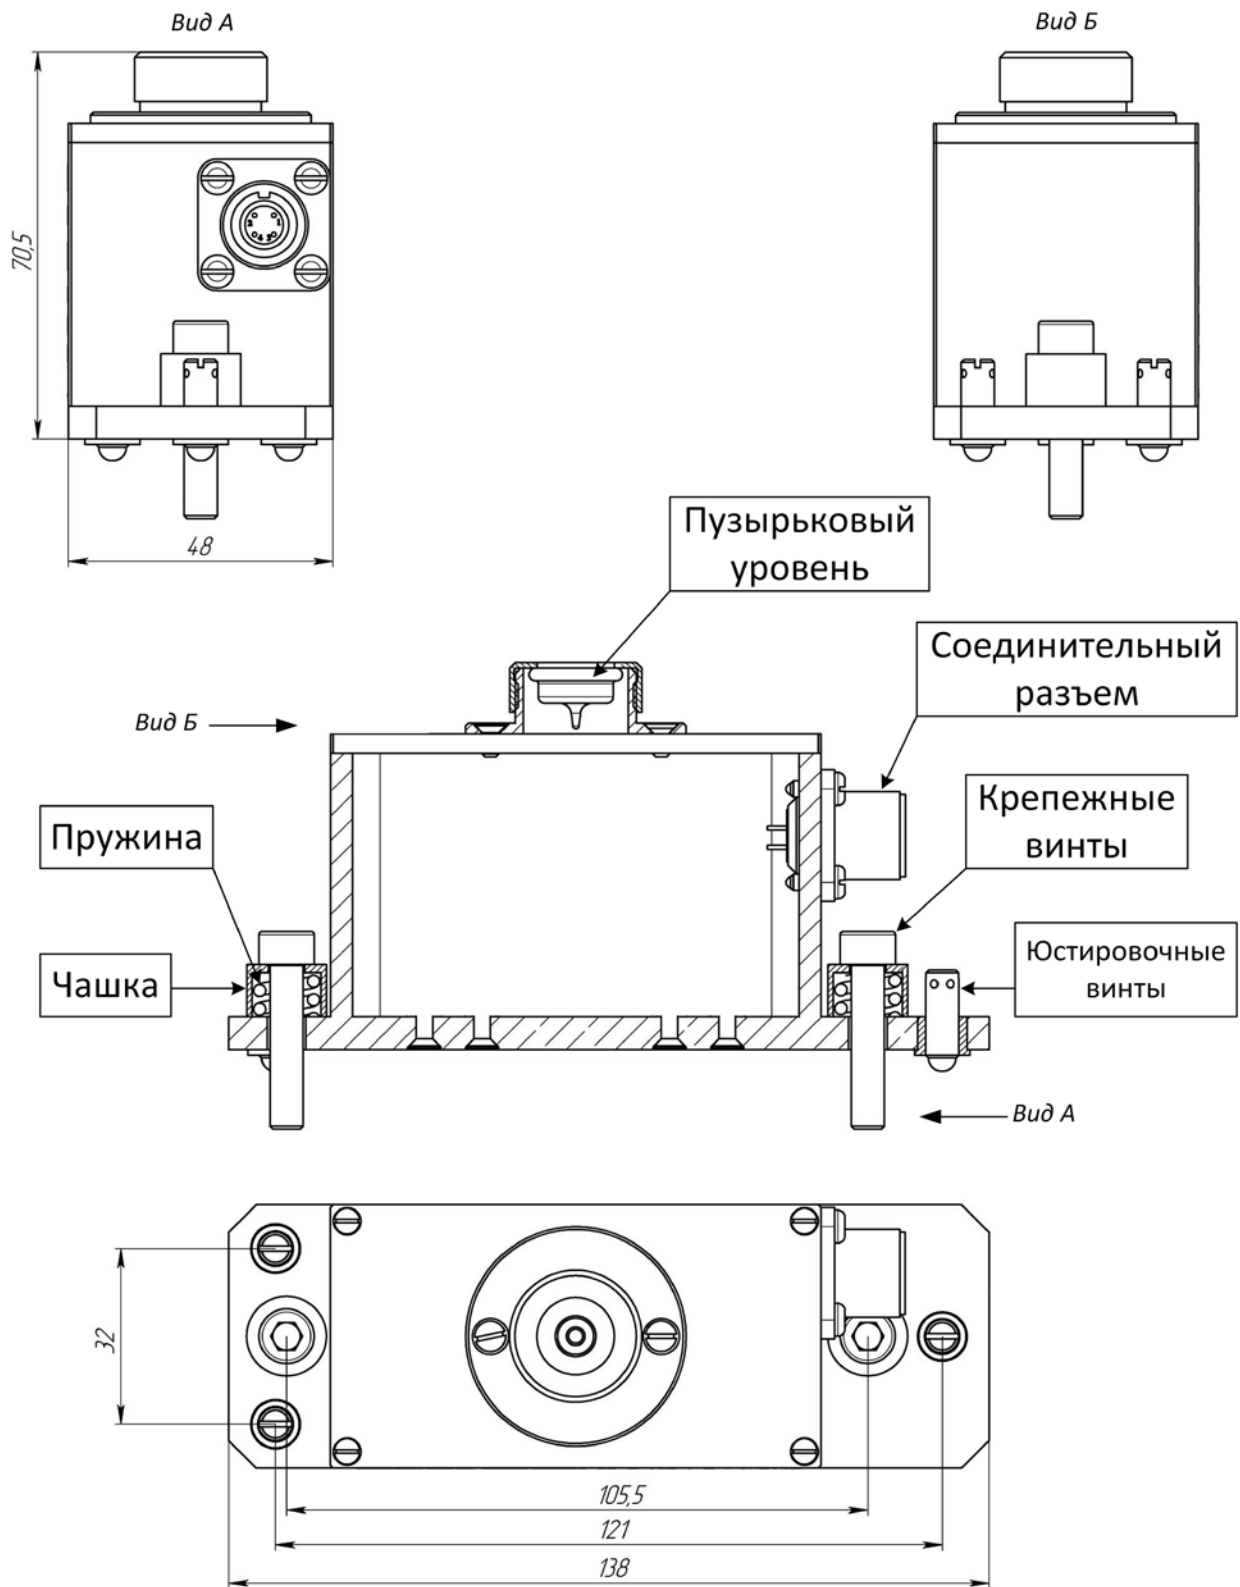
в Габаритные и присоединительные размеры датчика ВК-610.
